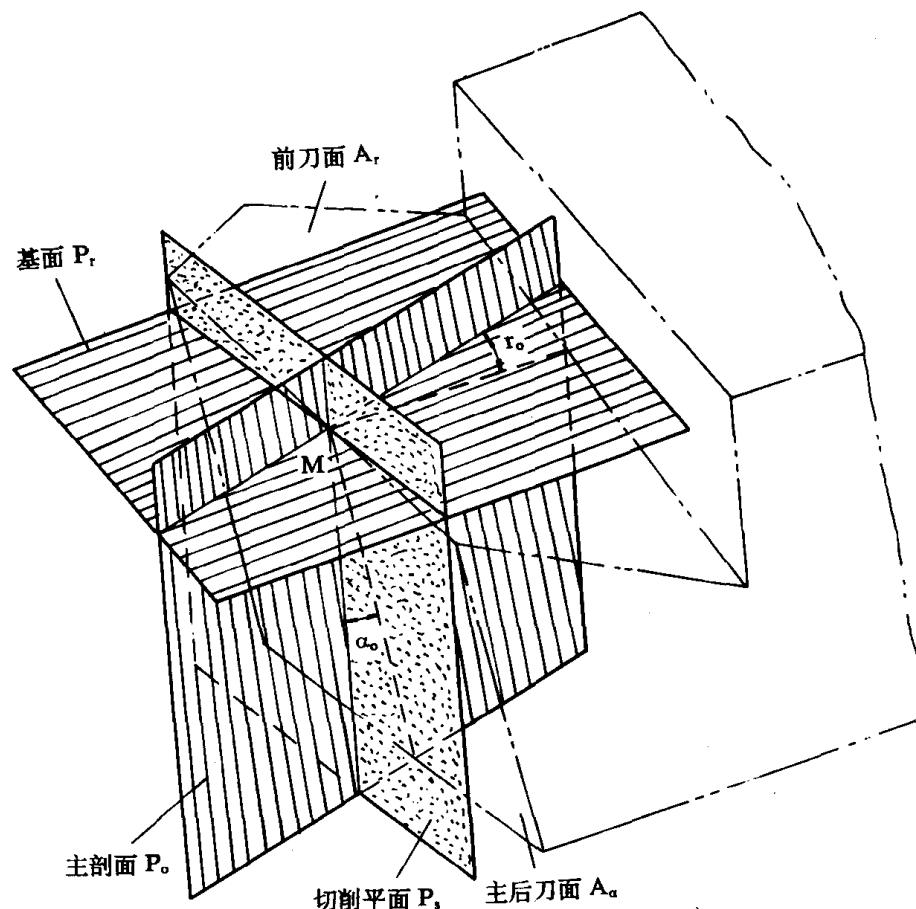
刀具标注角度坐标系（主剖面坐标系）
